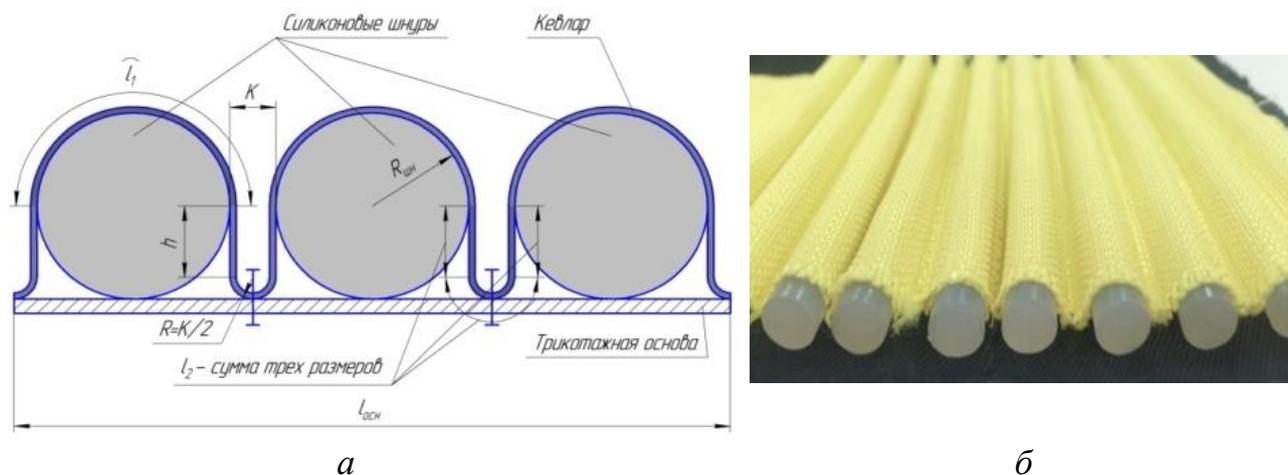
Динамические шумозащитные вставки: а – схема; б – образец
